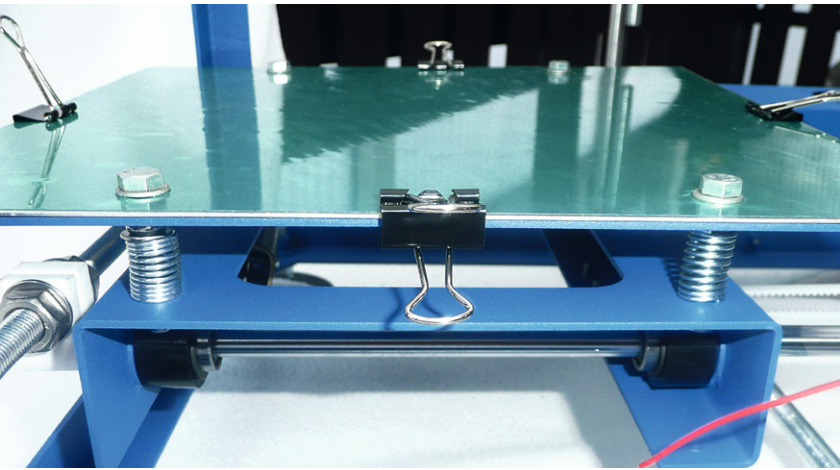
Die Befestigung des Druckbetts auf dem Schlitten mit Bolzen, siehe Text dazu. Die Nivellierung des Druckbetts erfolgt über die federbelasteten Bolzen.
